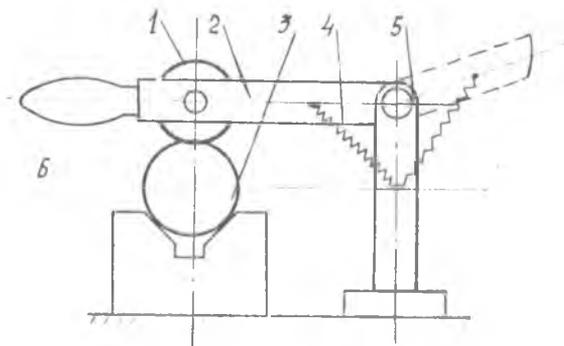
Рычажно-пружинный зажим: 1 — ролик; 2 — рычаг прижимной; 3 — деталь проверяемая; 4 — пружина; 5 — стойка; 6 — призма
